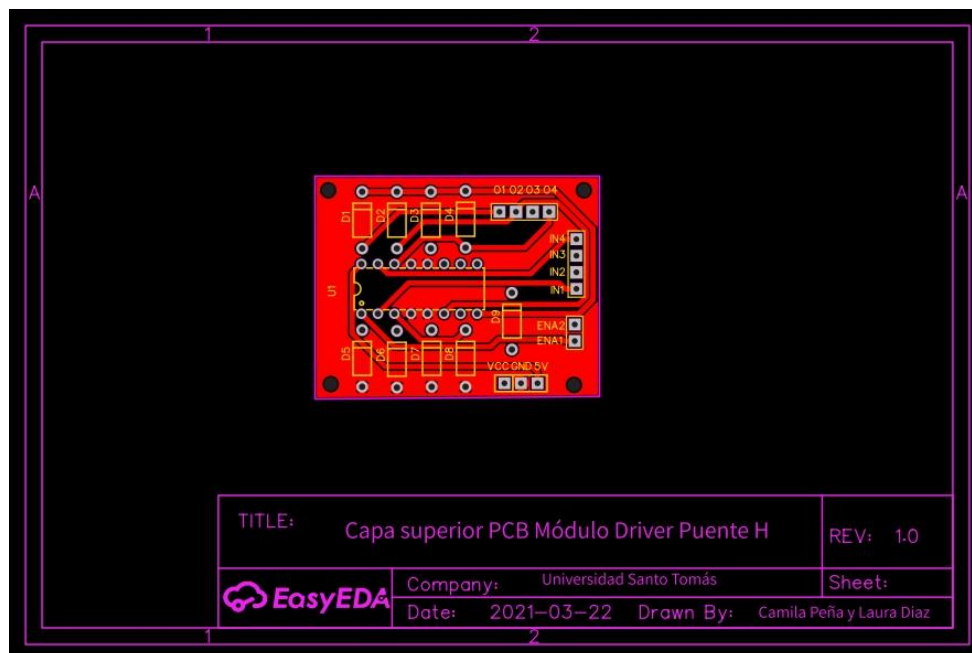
Diseño capa superior PCB módulo Driver Puente H.
